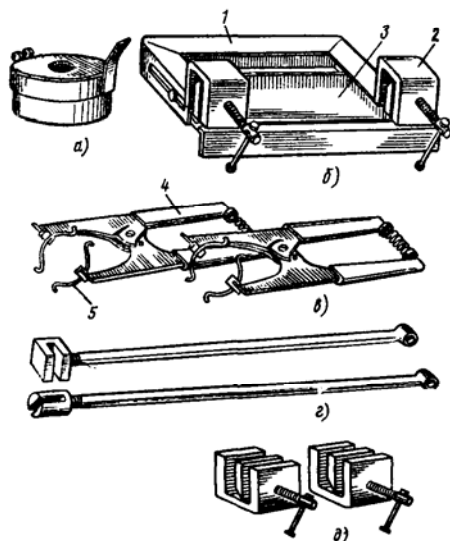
Принадлежности для термитно-тигельной сварки стальных полос и стержней заземления:
